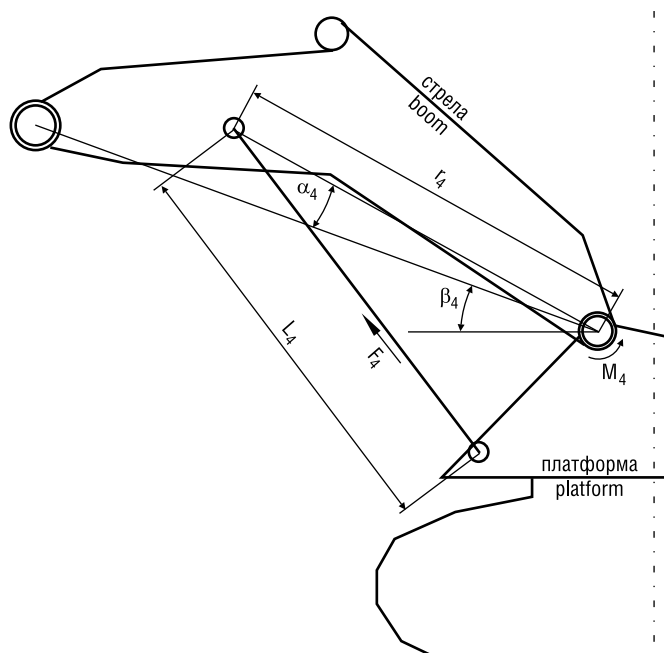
Кинематическая схема стрелы обратной гидролопаты:  $F_4$  – усилие, развиваемое гидроцилиндром рукояти;  $r_4$  – плечо, соединяющее ось крепления гидроцилиндра и стрелы и ось крепления стрелы и платформы;  $\alpha_4$  – угол между осью гидроцилиндра и плечом;  $M_4$  – момент вращения стрелы, развиваемый гидроцилиндром;  $L_4$  – длина гидроцилиндра (по центрам проушин);  $\beta_4$  – угол наклона стрелы / Fig. 5. Kinematic diagram of the backhoe boom:  $F_4$  is the force developed by the boom hydraulic cylinder;  $r_4$  is the lever connecting the mount axis of the hydraulic cylinder and the boom and the mount axis of the boom and the platform;  $\alpha_4$  is the angle between the hydraulic cylinder axis and the lever;  $M_4$  – the boom torque developed by the hydraulic cylinder;  $L_4$  – hydraulic cylinder length (by the centers of the eyelets);  $\beta_4$  – the boom tilt angle.
